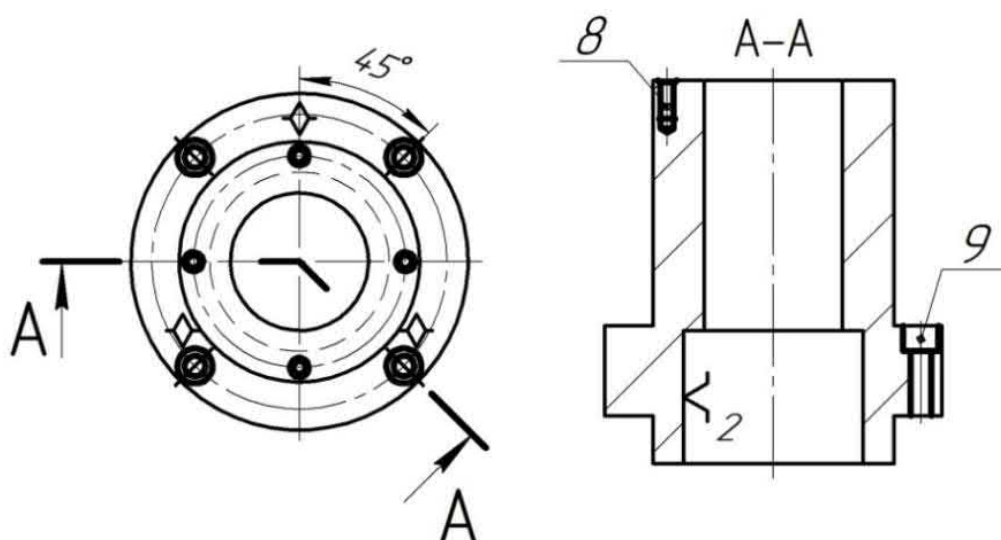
эскиз для фрезерной операции с ЧПУ 030 (установ. 1)
